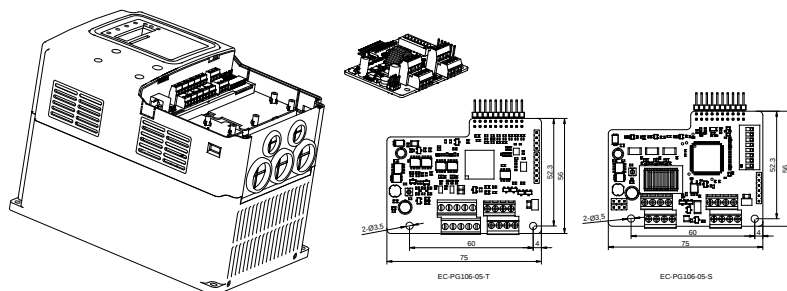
Размеры и схема установки EC-PG106-05-T (EC-PG106-05-S)
